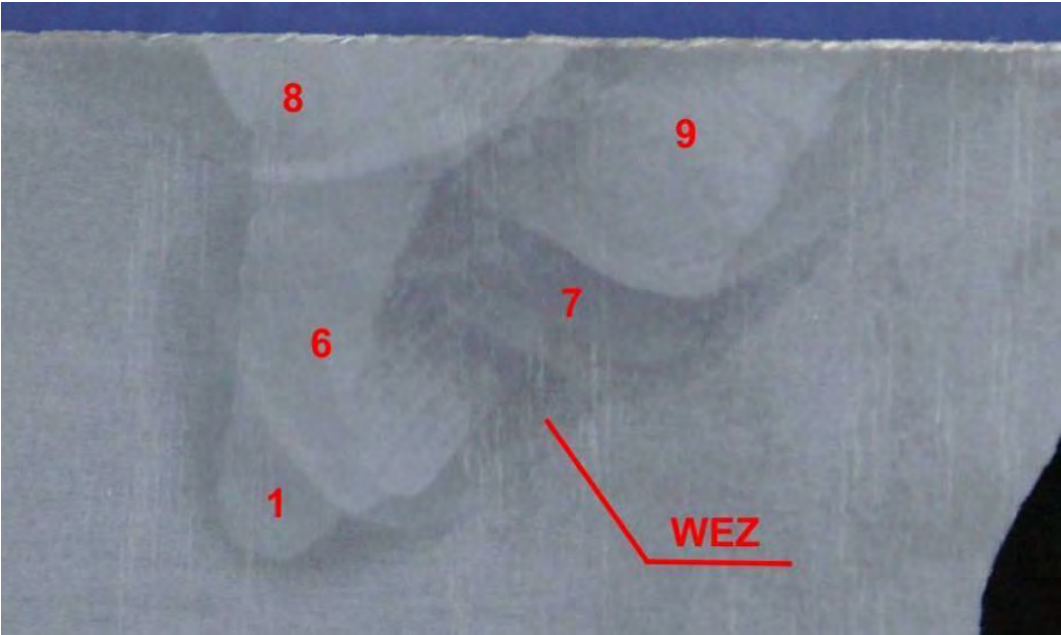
Probe 02 - Ansicht oberer Teil der Schweißnaht
